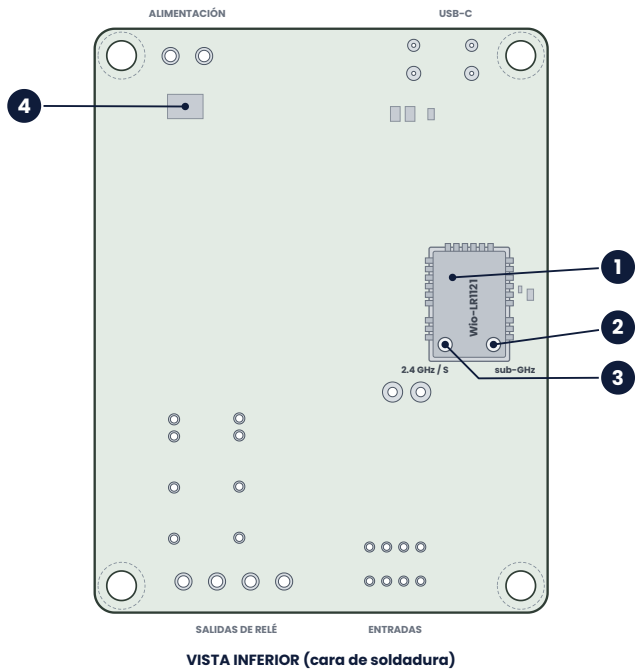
Vista inferior: el módulo LoRa y sus dos conectores de antena están en la cara de soldadura.
